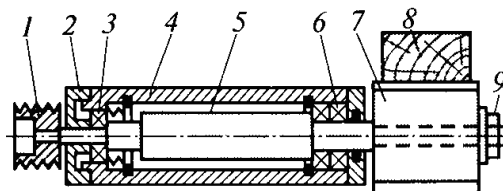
Принципова схема горизонтального шпиндельного блоку: 1 – шків; 2 – кришка; 3 – задня опора; 4 – гільза; 5 – шпиндель; 6 – передня опора; 7 – різальний інструмент; 8 – заготовка; 9 – гайка
